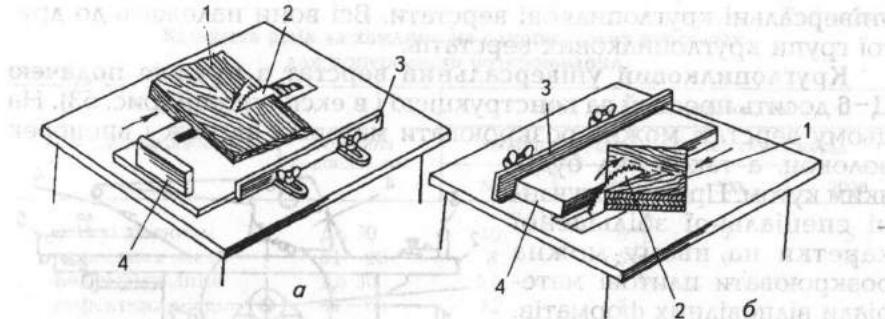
Пристрій для поперечного розкроювання на універсальному верстаті:
